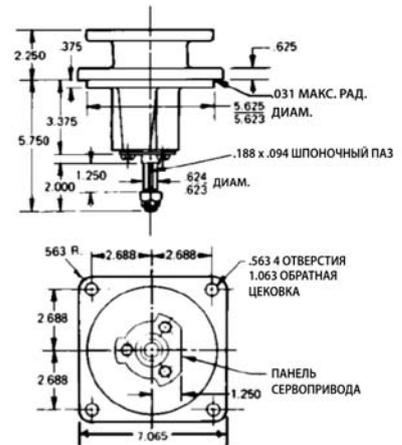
Габаритный чертеж PGA с вращающимся выходом (79 Дж), базой UG-40 и управлением нагрузкой (не использовать в конструировании)
